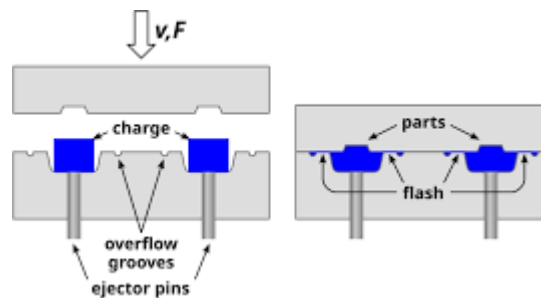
Moulage par compression de mat pré imprégné SMC.
